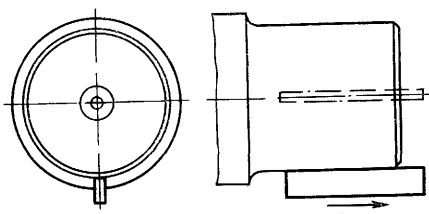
Проверка прямолинейной образующей посадочной поверхности вала
